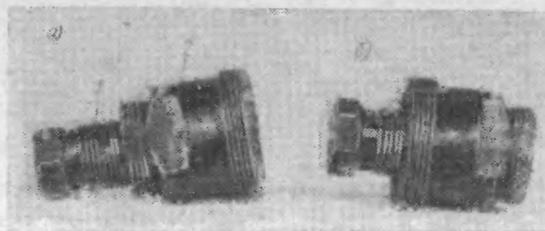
Положение съемника для вывертывания ведущей звездочки и шестерни муфты сцепления (*а*) и положение съемника для вывертывания ведущей шестерни (*б*);
